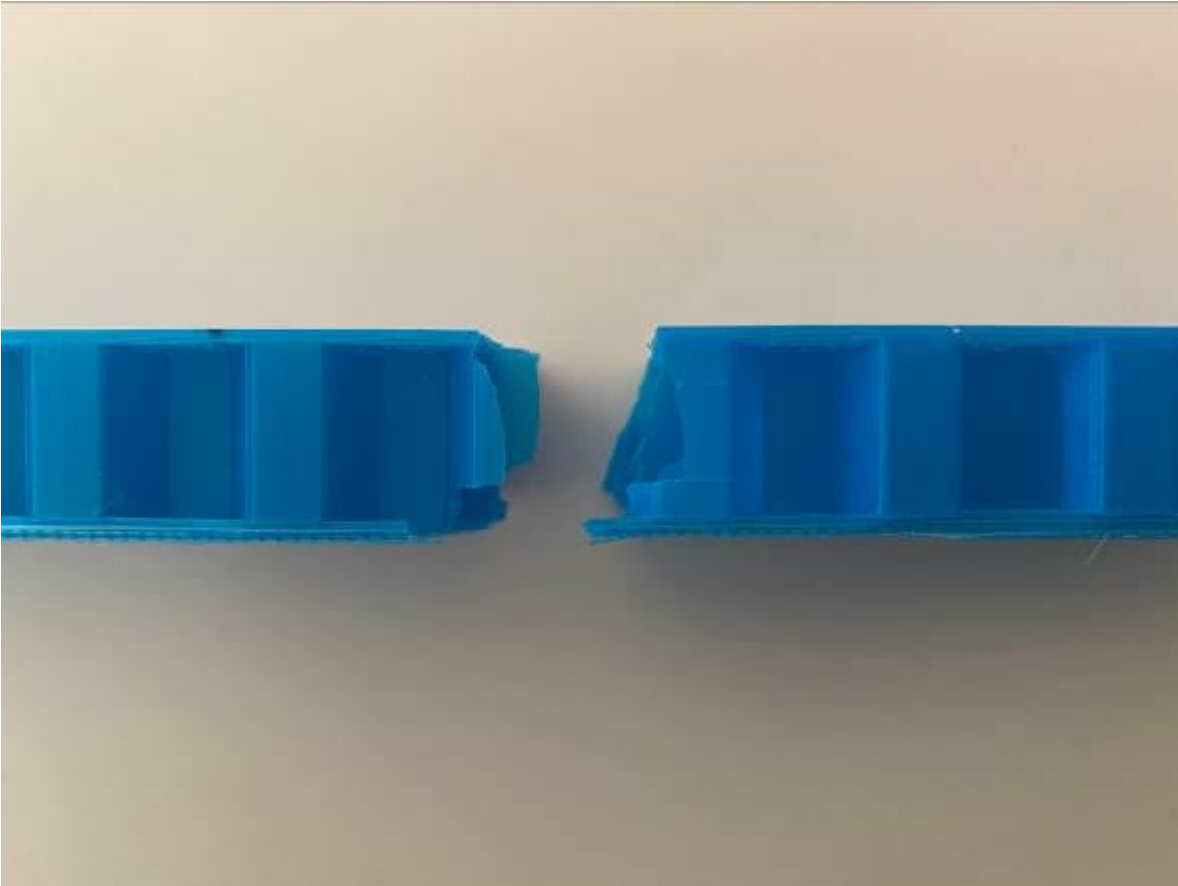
Espécimen 2 del lote de 3/8" fabricado completamente en PLA con tratamiento térmico, tipo de falla X-A-F.
